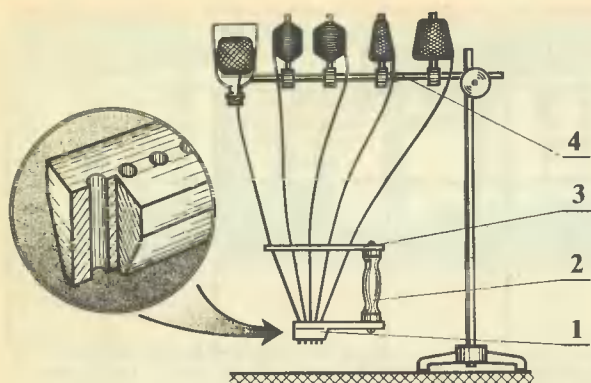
Приспособление для нанесения ворсового покрытия параллельными рядами: 1 — нижняя пластина с накопечником, 2 — рукоятка, 3 — направляющая пластина, 4 — кронштейн.
